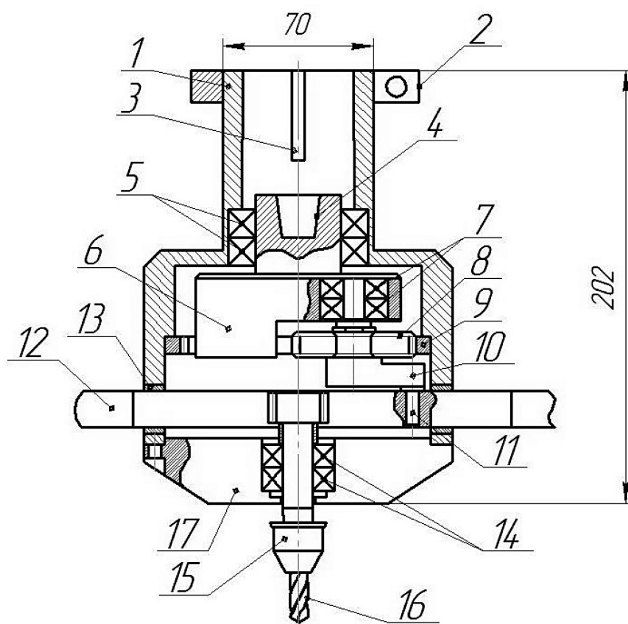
Схема та вигляд пристрою для реверсивного свердління.
